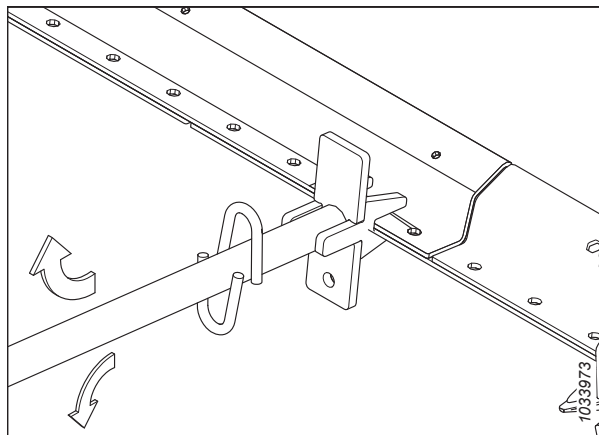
Регулировка пальцевого бруса — без противорежущих пальцев
